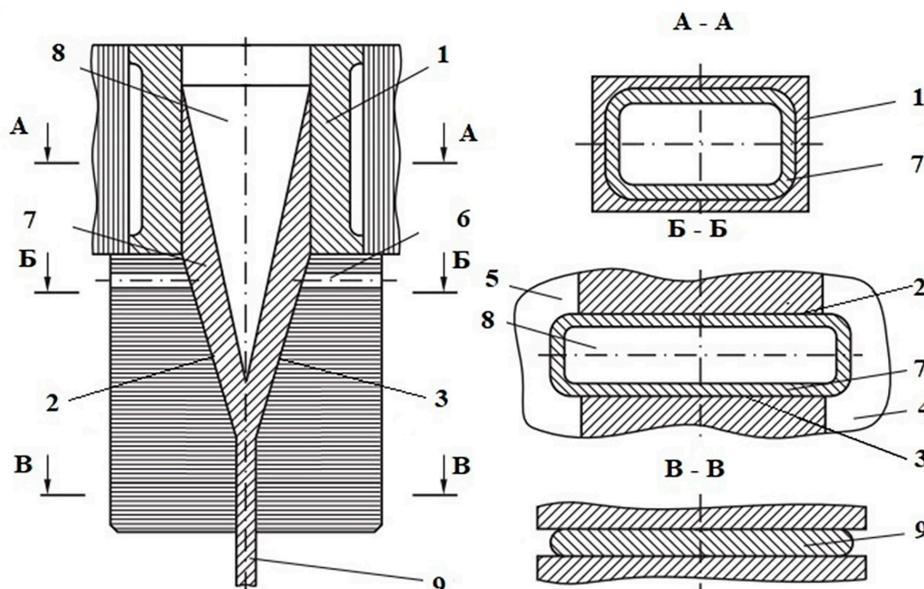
Схема комплекта агрегатов МНЛДЗ в сборе:
